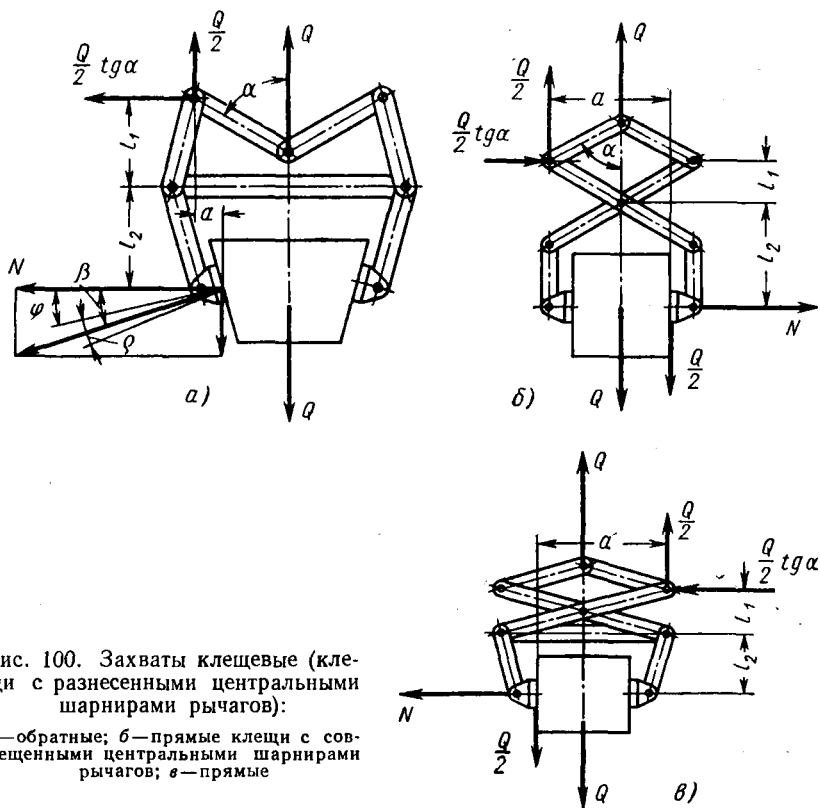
Захваты клещевые (клевцы с разнесенными центральными шарнирами рычагов):
